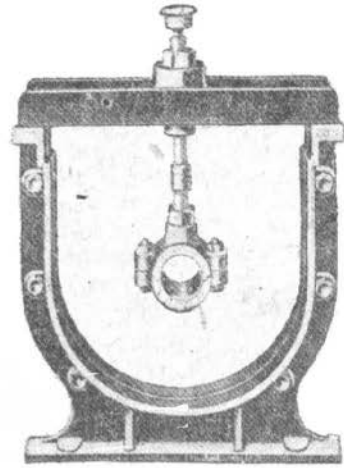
Концевая стойка шнека с отлитым заодно подшипником.
